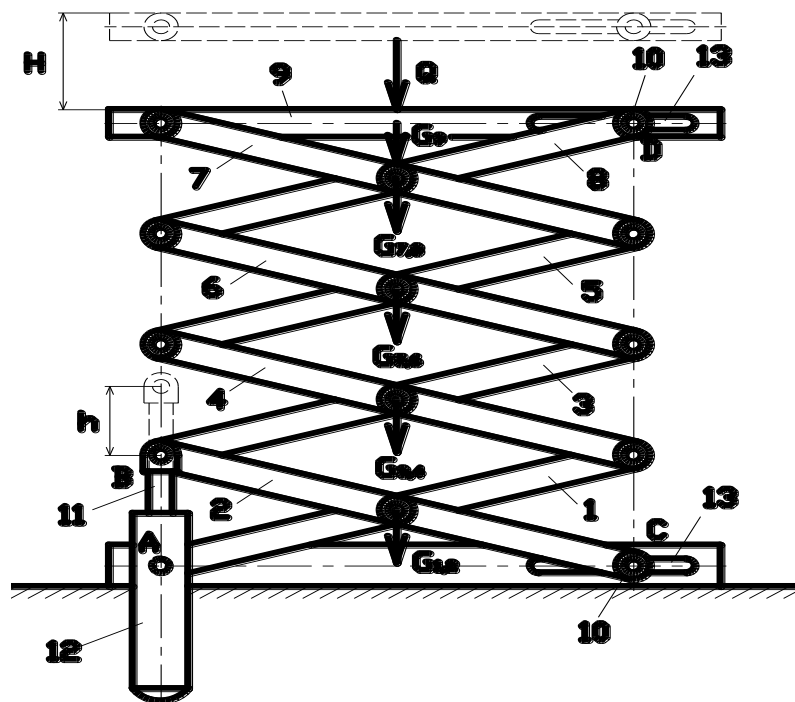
Шарнирно-рычажный механизм привода ножничного подъемника
